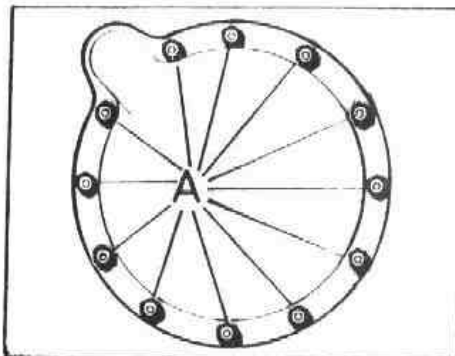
Desmontaje de tuercas de unión caja de cambios a motor
